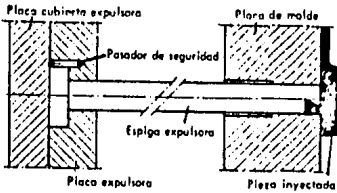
Botador con entalla en el extremo para retener la pieza inyectada al abrir el molde.
